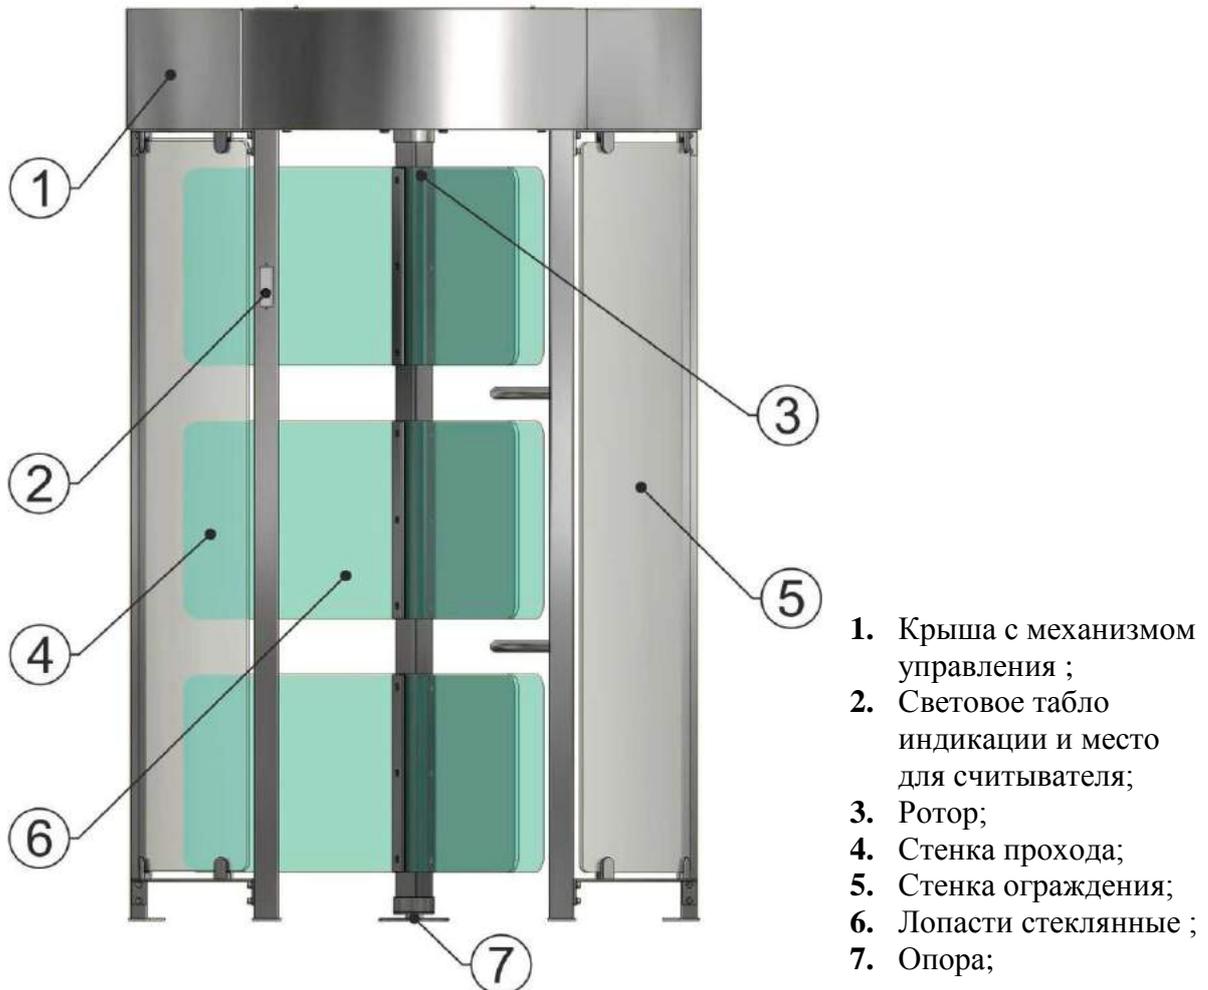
Конструкция и общий вид турникета «GlassGo» АЮИА.436
